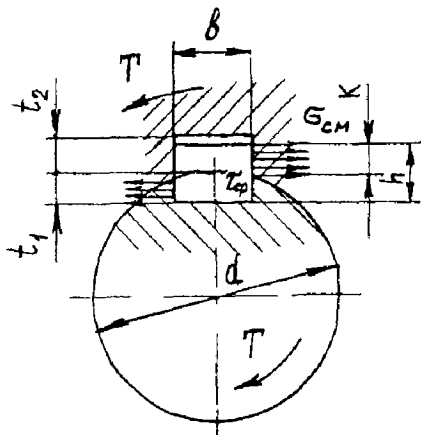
Поперечний перетин шпонкового з'єднання
